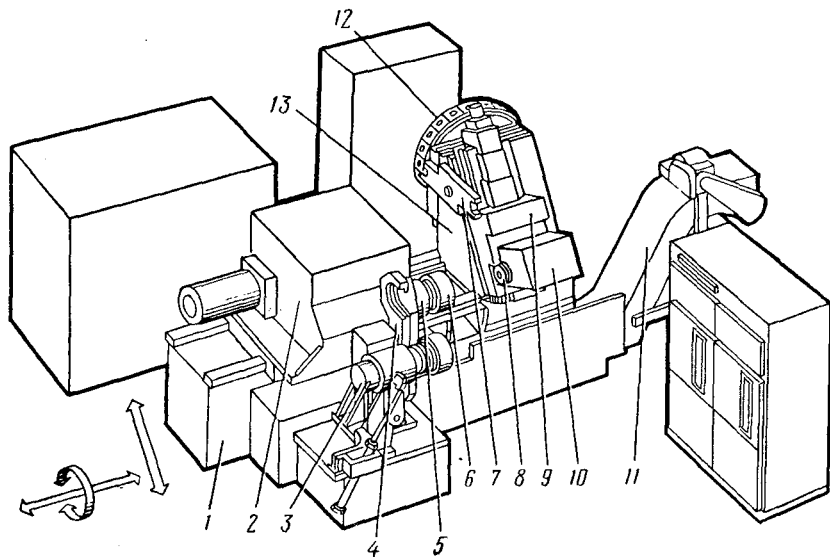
Токарный «обрабатывающий центр» фирмы «Kearney and Trecker»
